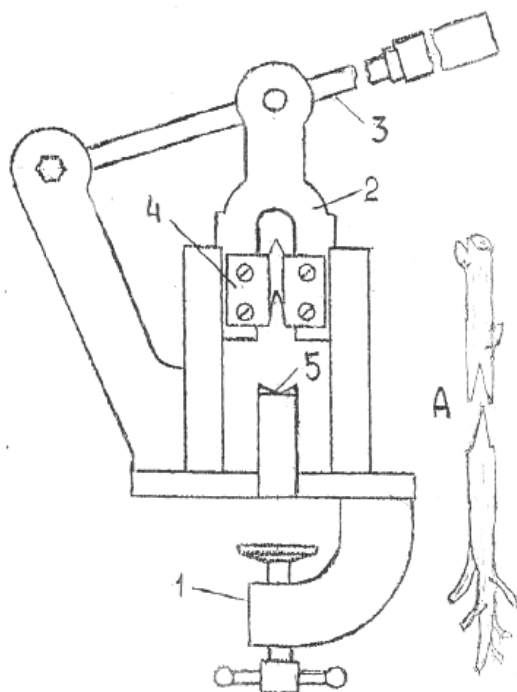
Схема механического устройства с клинообразным ножом: 1 – станина; 2 – ползун; 3 – рычаг; 4 – клинообразный нож; 5 – противорез. А – вид выполненных срезов
